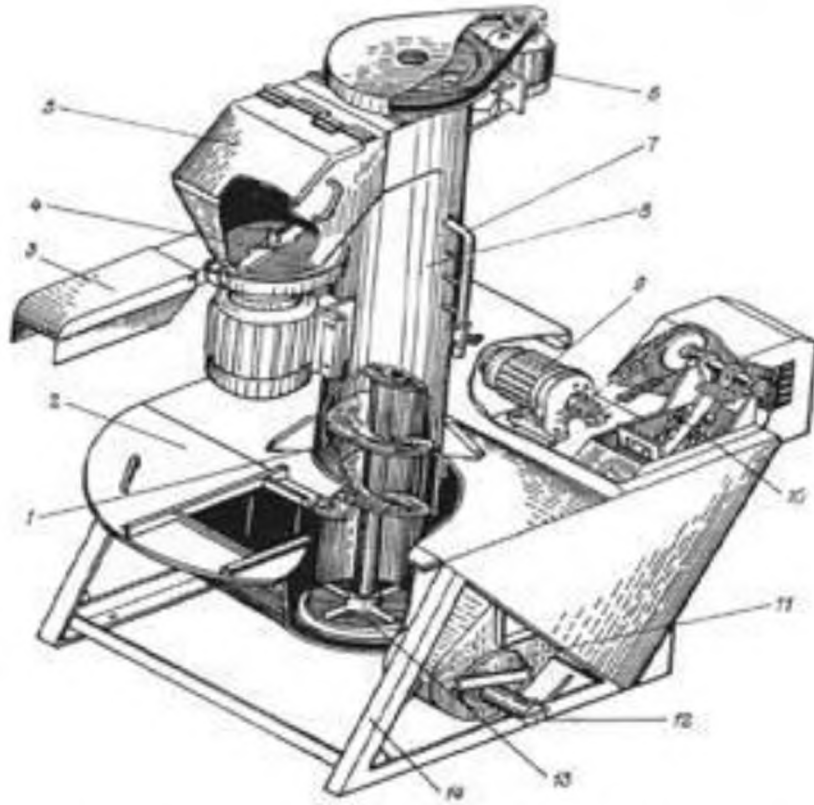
Подрібнювач – каменеуловлювач ИКМ - 5 1 – живильний шнек; 2 – ванна; 3 – лоток; 4 – подрібнюючий апарат; 5 – кришка; 6 – електродвигун; 7 – водяний патрубок; 8 – корпус шнека; 9 – мотор-редуктор привода транспортера; 10 – скребковий транспортер; 11 – люк; 12 – клапан; 13 – крильчатка; 14 – рама.
